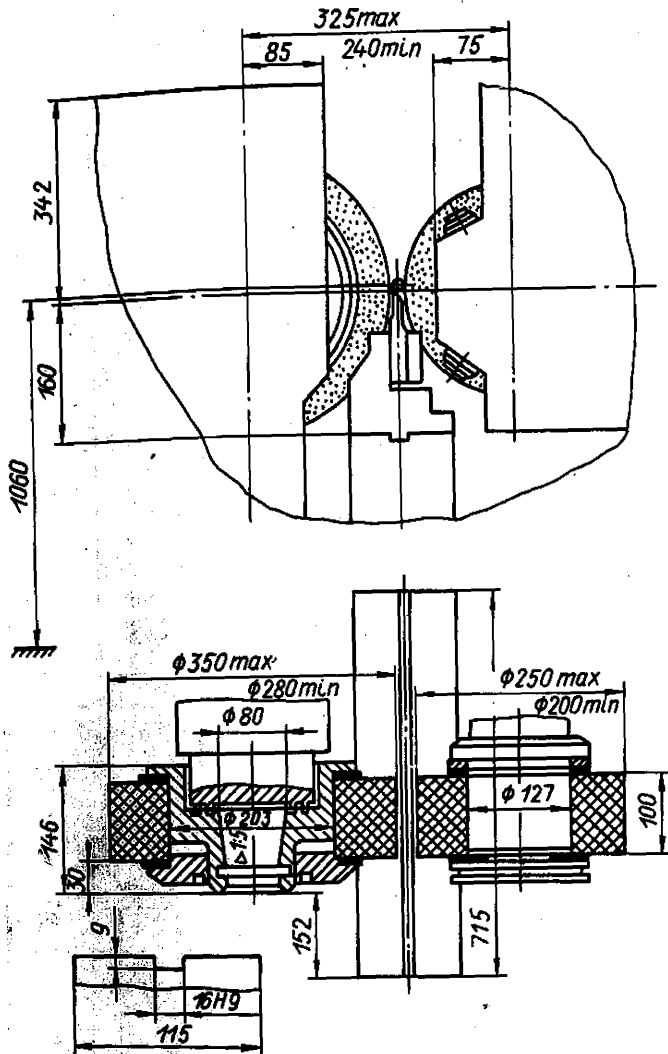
Габаритные размеры рабочей зоны, посадочных и присоединительных баз станка ЗМ182
